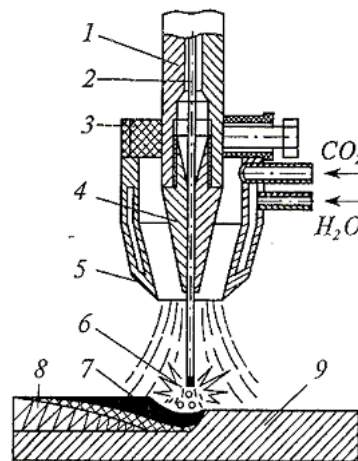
Схема наплавки в среде углекислого газа: 1 – мундштук; 2 – электродная проволока; 3 – горелка; 4 – наконечник; 5 – сопло горелки; 6 – электрическая дуга; 7 – сварочная ванна; 8 – наплавленный металл; 9 – наплавляемая деталь
